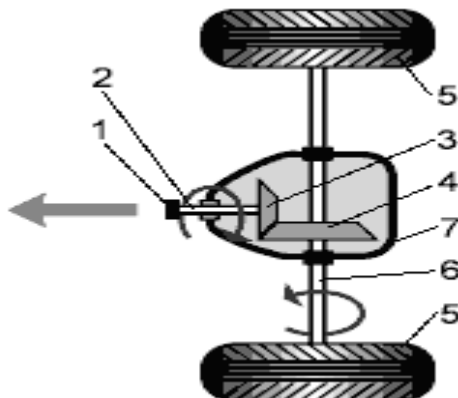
Схема работы главной передачи 1 - фланец; 2 - вал ведущей шестерни; 3 - ведущая шестерня; 4 - ведомая шестерня; 5 - ведущие (задние) колеса; 6 - полуоси; 7 - картер главной передачи
